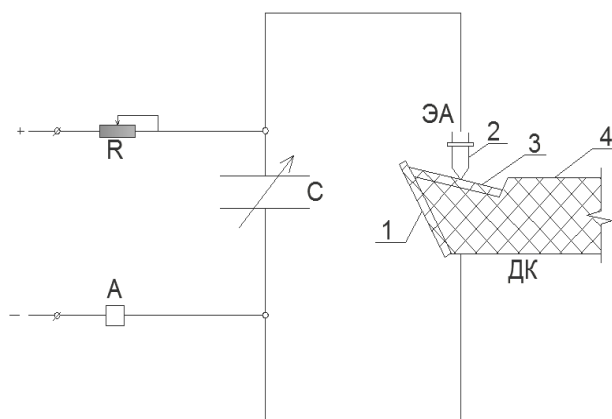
в - принципиальная схема установки: 1 - графитовая пластина; 2 - электрод; 3 - упрочняемая поверхность; 4 - корпус инструмента; ДК - деталь - катод на контактной пластине; ЭА - электрод - анод
